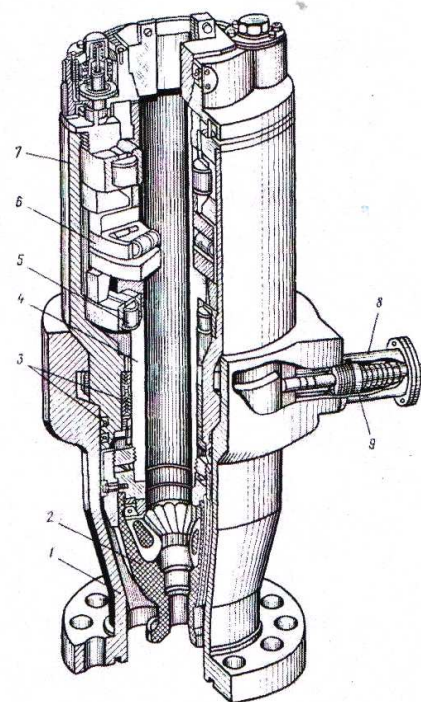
Вращающийся превентор ВП-156х320: 1-корпус; 2-уплотнитель; 3-манжетные уплотнения; 4-ствол; 5-радиальные подшипники; 6-упорный подшипник; 7-патрон; 8-штуцер; 9-защелка
